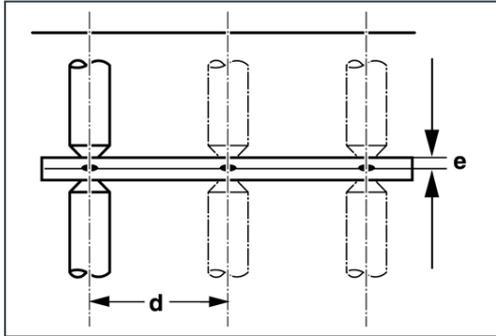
rapport épaisseur de tôle/écart entre les points de soudage
